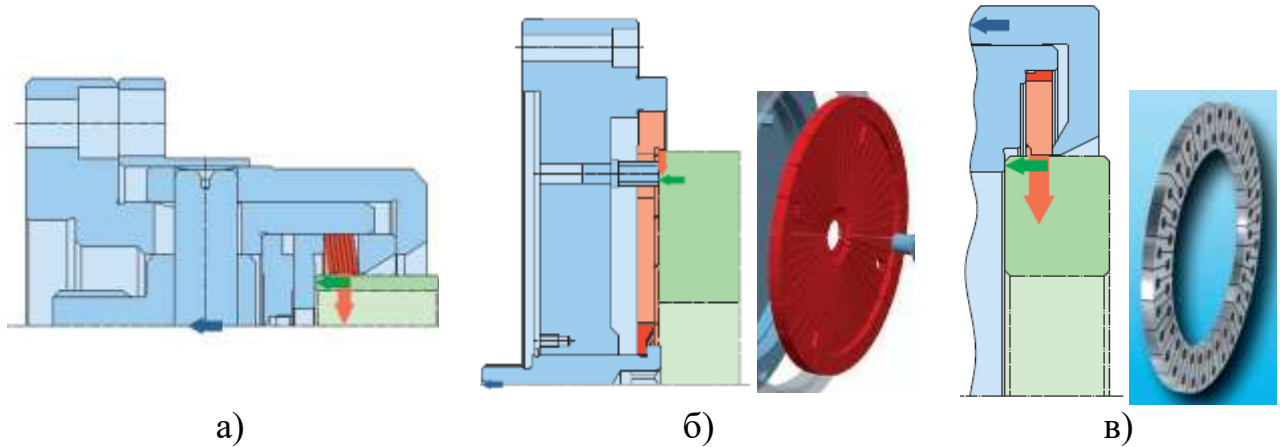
Схеми затискних патронів з пружними елементами фірми Ringspann GmbH
